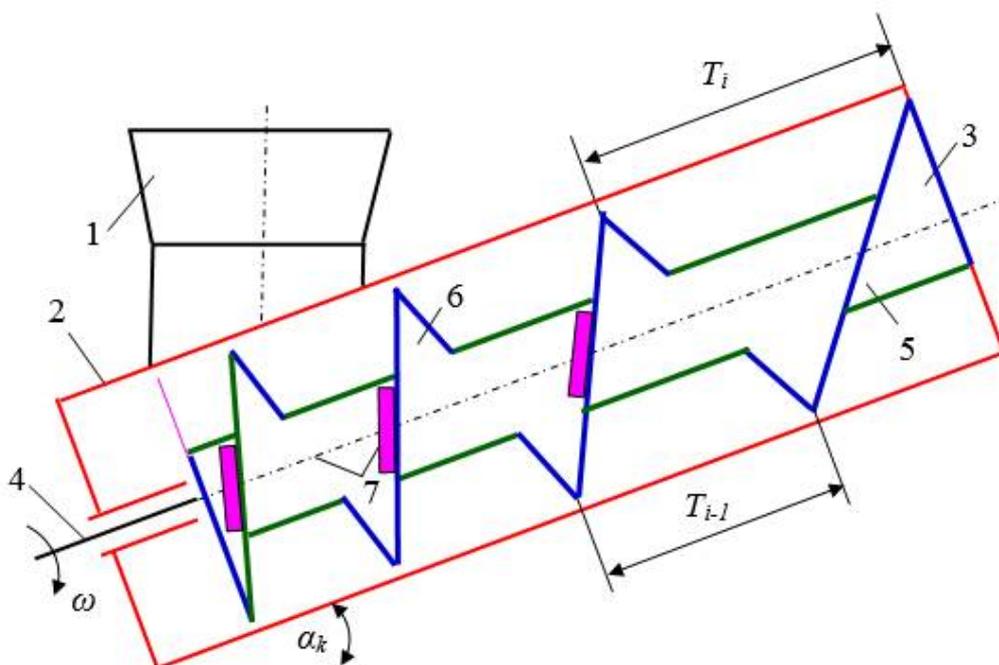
Конструктивно-компонувальна схема удосконаленого шнекового транспортера-подрібнювача: 1 – завантажувальний бункер; 2 – напрямна труба; 3 – шнековий конвеєр; 4 – приводний вал; 5 – барабан; 6 – спіральний виток; 7 – ніж-подрібнювач
